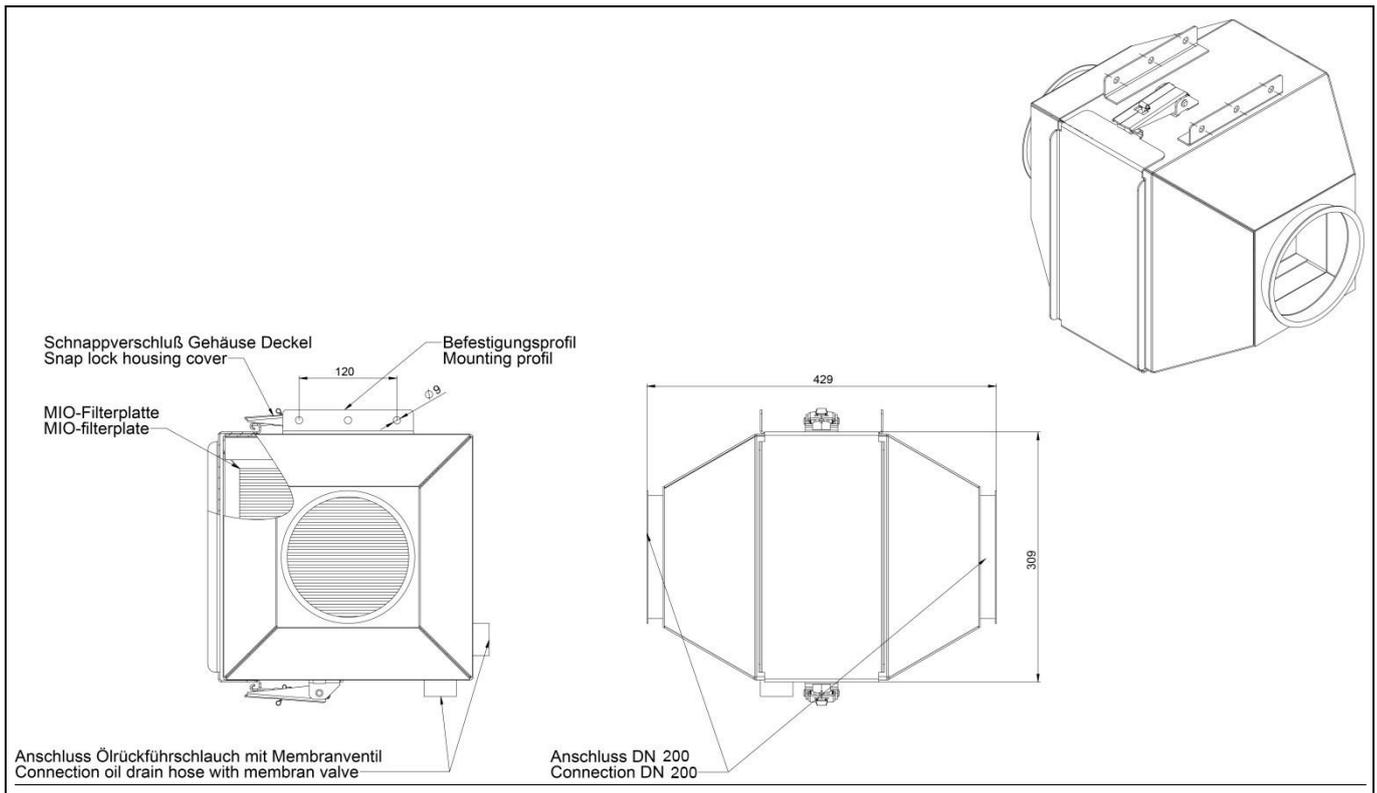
Montage einer Filterplatte außerhalb einer Bearbeitungsmaschine
